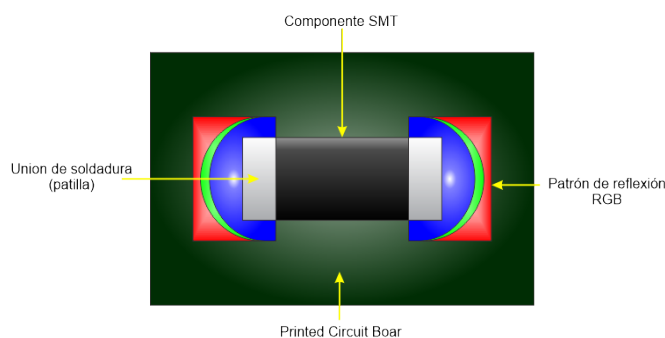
Patrón de reflexión RGB sobre la unión de soldadura de un componente SMT
